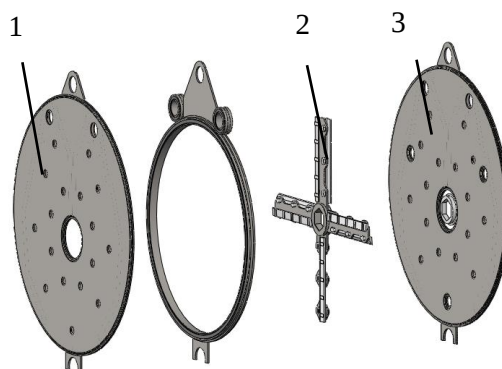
Основные конструктивные элементы пластинчатого скребкового теплообменника: 1 – сварная теплообменная пластина; 2 – уплотнительное кольцо; 3 – нож-мешалка
